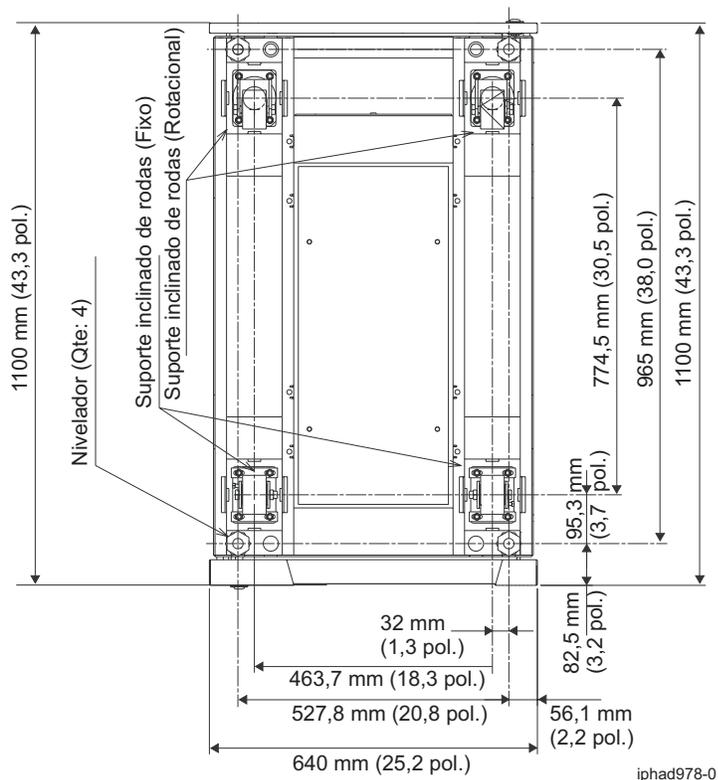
Locais do nivelador e do suporte inclinado de rodas
